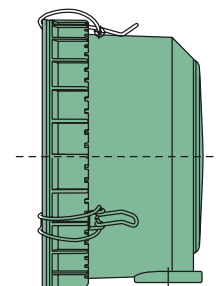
Parte inferior do corpo com fechos de arame (em 45 280 ... até ... 45 680)
